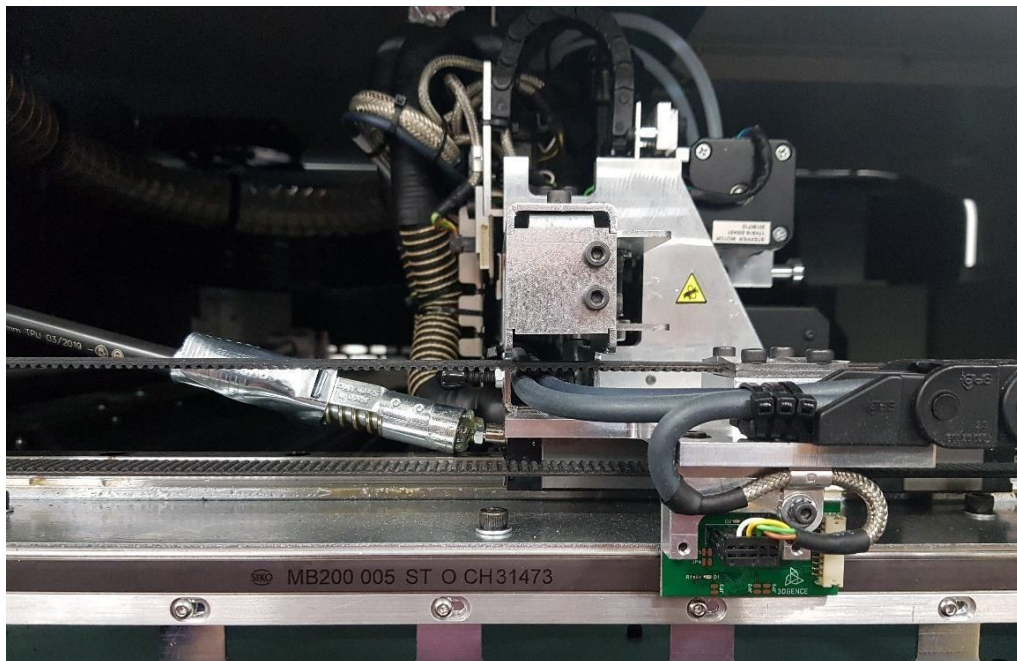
Подача смазки в смазочные ниппели в левой части принтера
